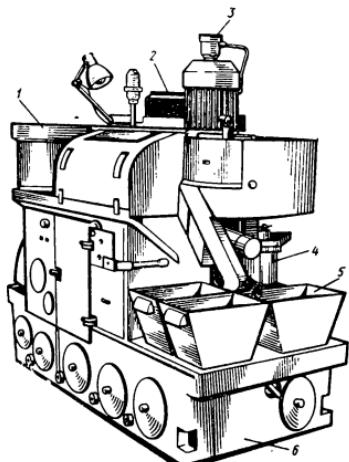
Непрерывно-протяжной автомат ДТГ2 с движением заготовки:
